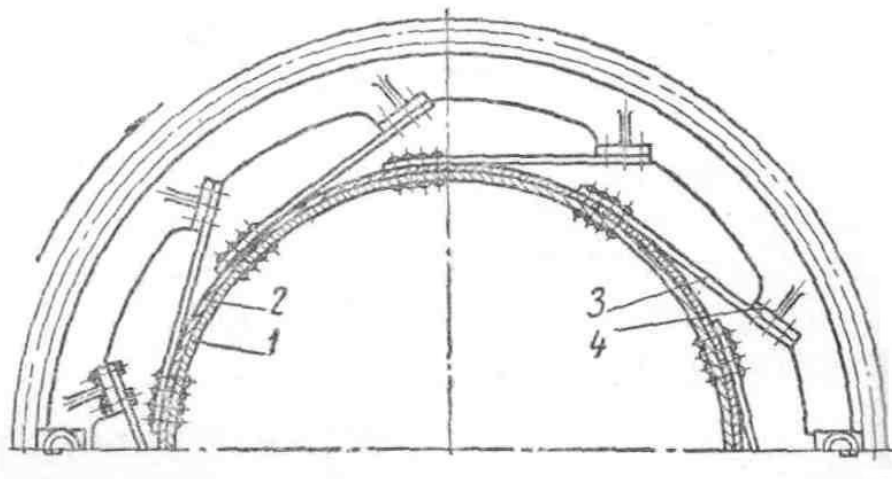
Кріплення вінцевої шестерні до барабана тангенціальними пружинами: 1 – барабан; 2 – пояс жорсткості; 3 – плоска пружина; 4 – лапа шестерні
